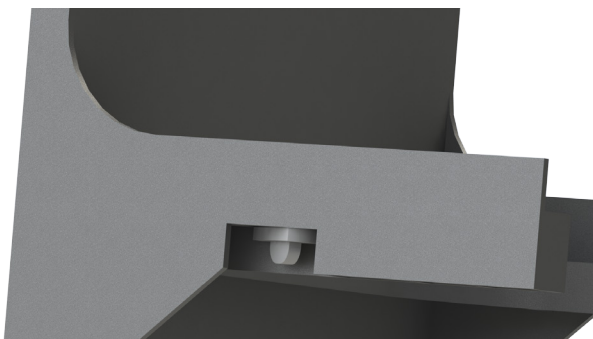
Zijaanzicht SPARK - beschikbare ruimte voor bevestiging
